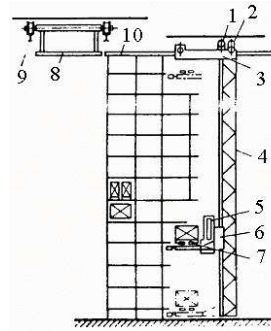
Стеллажный кран-штабелер с одной грузоподъемной колонной с опорой на стеллажи
